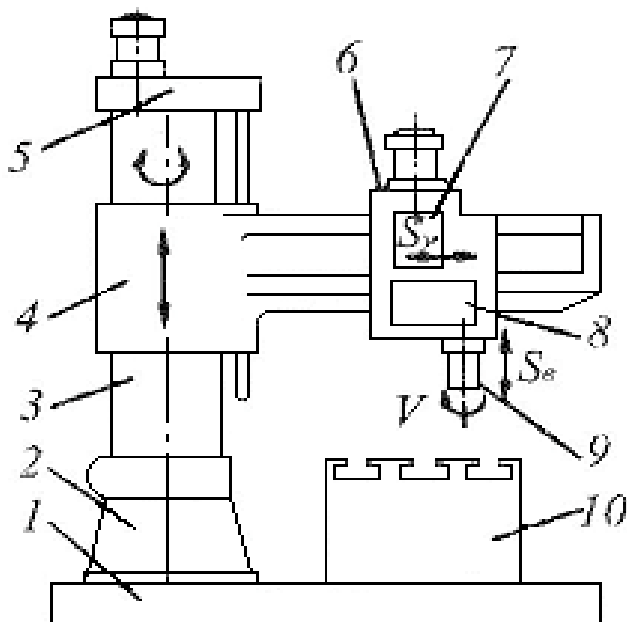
Загальний вигляд радіально-свердильного верстата
